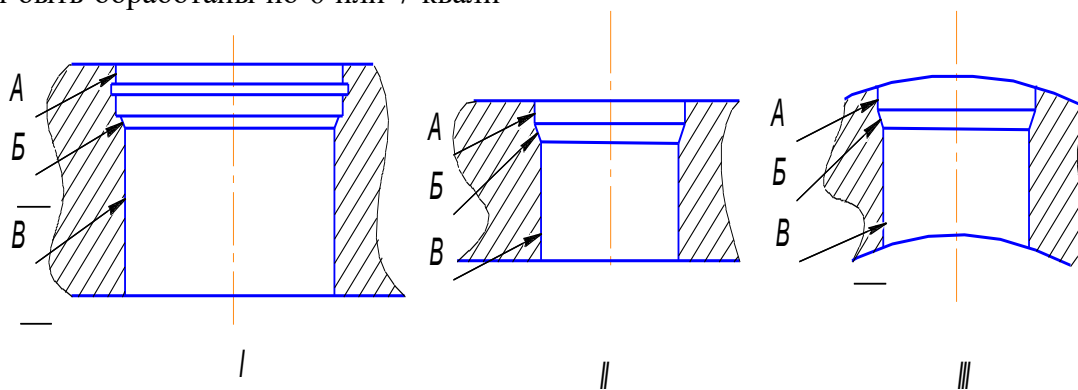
Основные типы ступенчатых отверстий корпусных деталей
